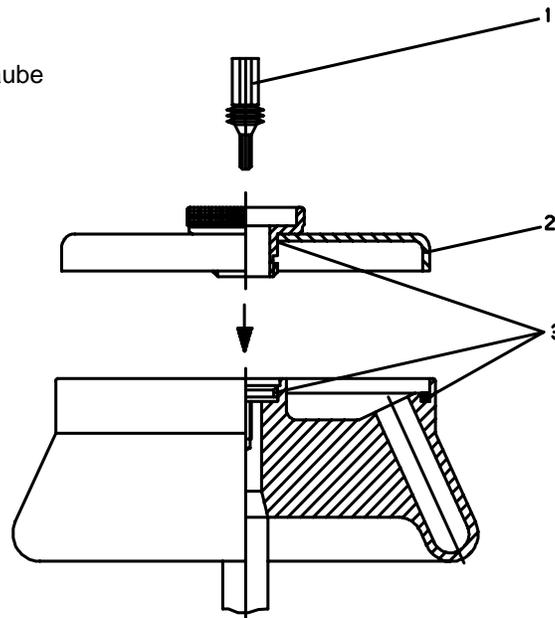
Winkelrotor mit hermetisch verschließbarem Deckel
